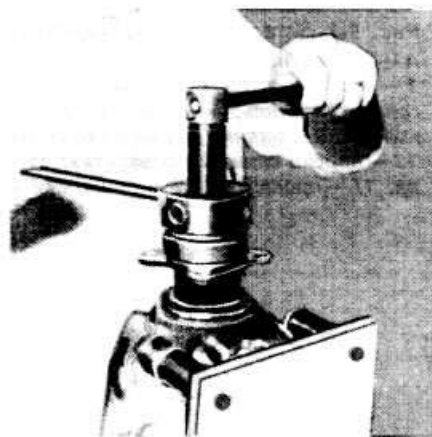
Установка фланца ведущей шестерни с помощью приспособления 23 13 00
